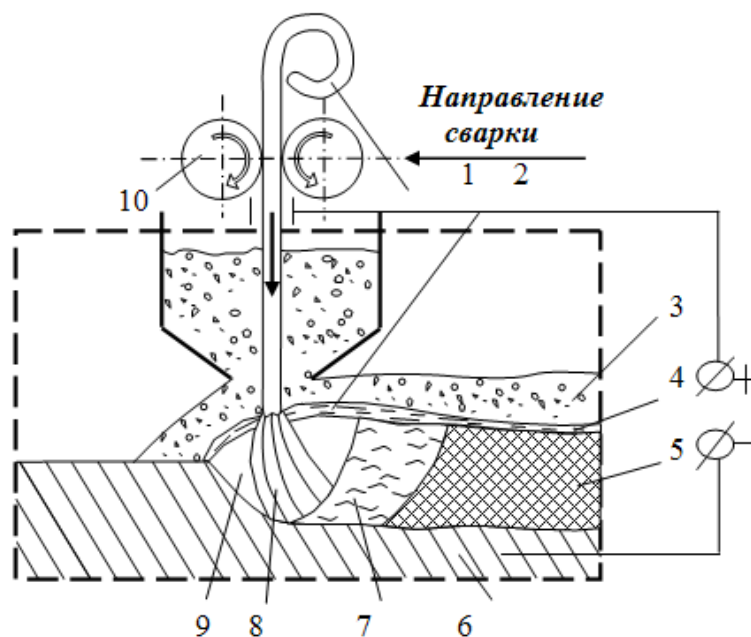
Схема процесса автоматической сварки под слоем флюса: 1 —электрод; 2—жидкий флюс; 3 — сыпучий флюс; 4—спекшийся флюс; 5—закристаллизовавшийся металл шва; 6 — свариваемый металл; 7 — расплавленный металл шва; 8 — зона электрической дуги; 9 — газовый пузырь; 10 — подающие ролики.
